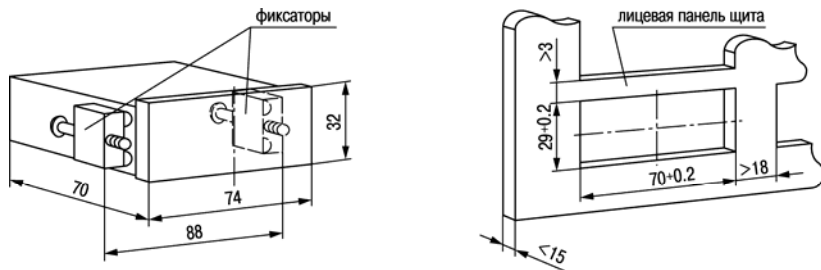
Габаритные и установочные размеры ТРМ501
